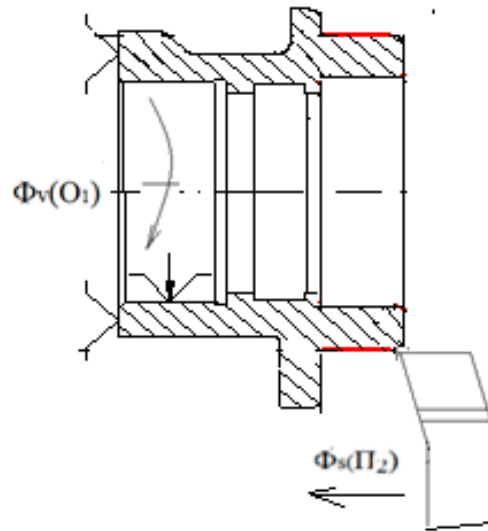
Рухи при обробленні зовнішньої поверхні
